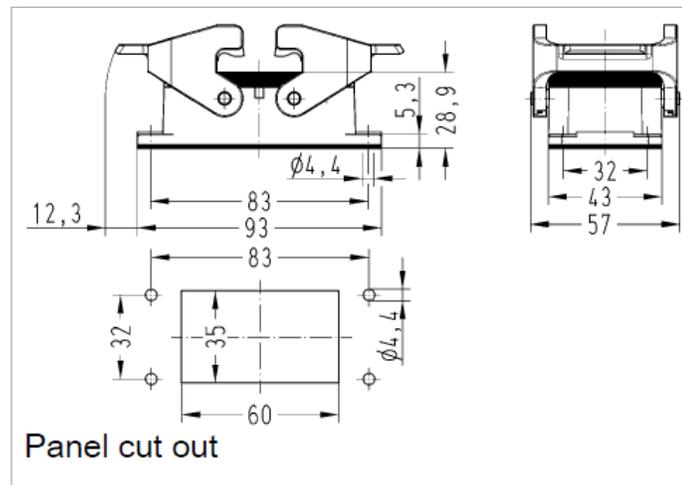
Dimensiones del inserto Harting Han 10 E®
